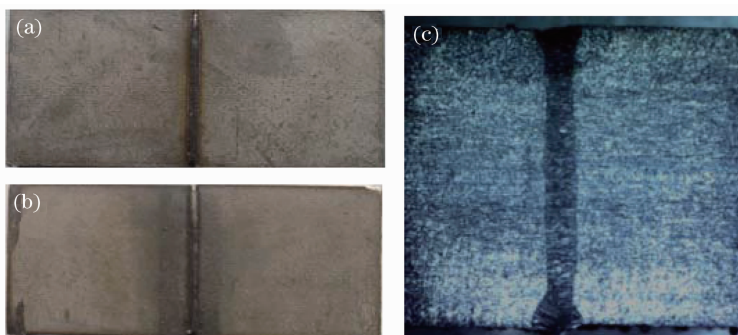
焊缝形貌。(a) 焊缝正面;(b) 焊缝背面;(c) 焊缝截面
